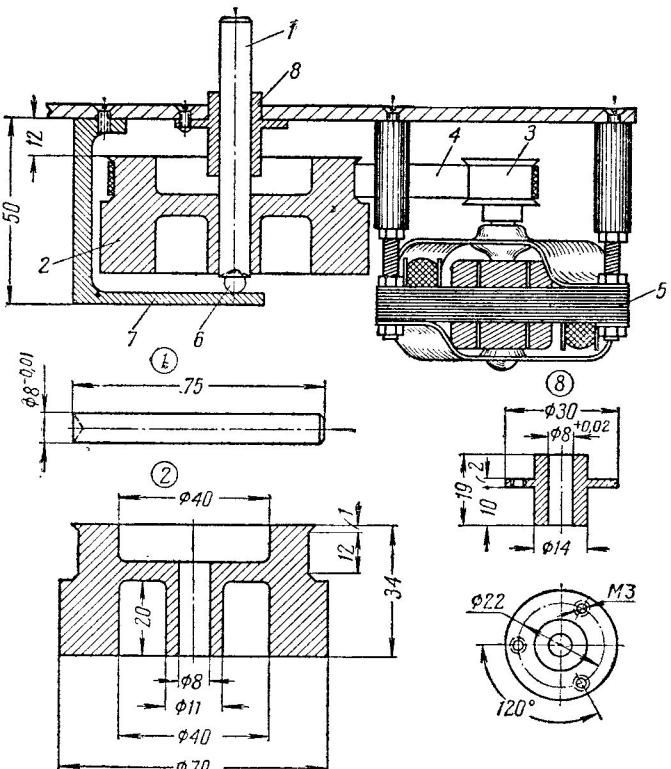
Ведущий узел лентопротяжного механизма: 1 — ведущий вал, 2 — маховик (диаметр рабочей части 60 мм), 3 — шкив двигателя (диаметр 10 мм), 4 — пасик, 5 — ведущий двигатель, 6 — шарик, 7 — скоба, 8 — втулка. У вращающихся деталей рабочие размеры приведены для скорости 190,5 мм/сек.
